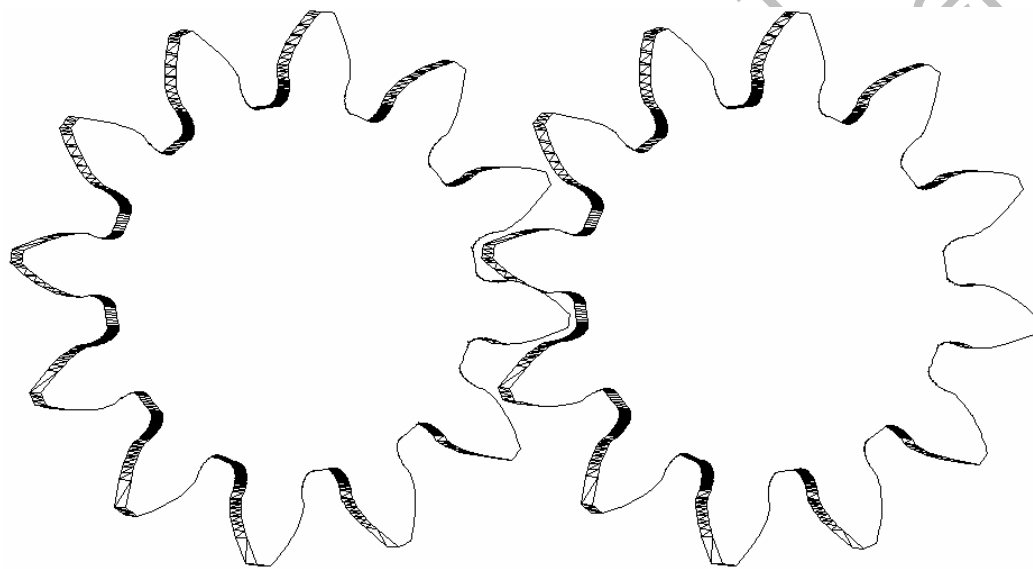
Пример твердотельной зубчатой передачи в сборе
